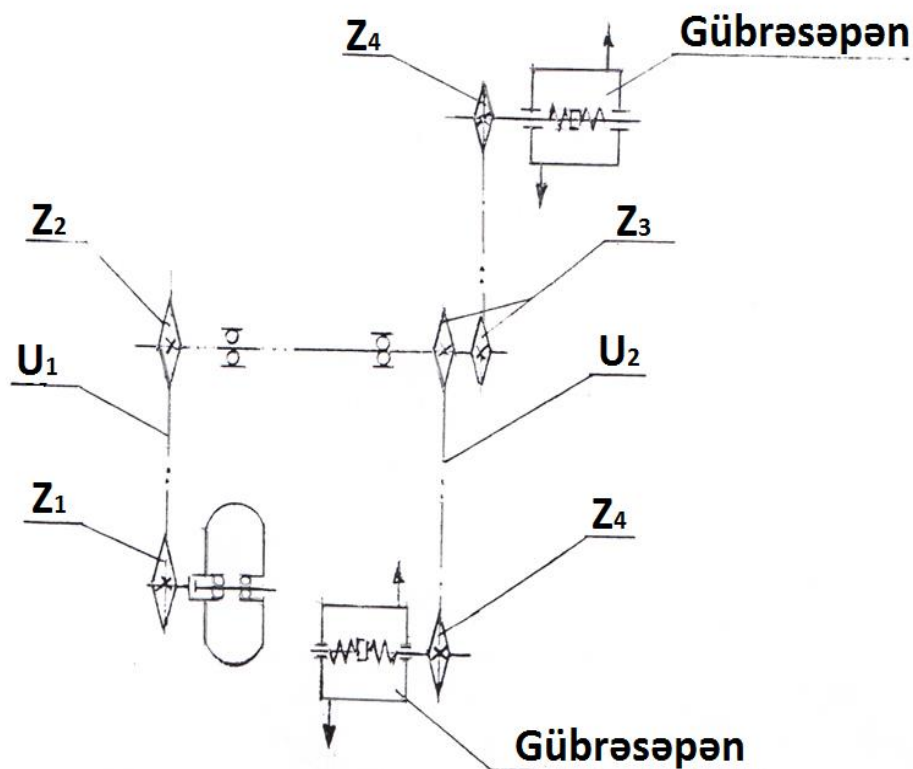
кинематическая схема разбрасывателя удобрений
